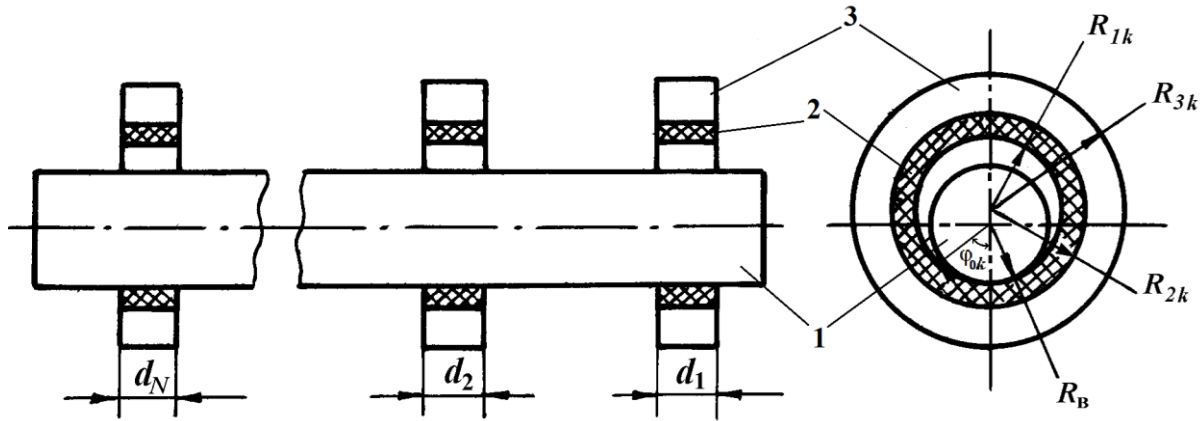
Схема системы подшипников на общем валу. 1 – вал, 2 – полимерная втулка, 3 – корпус
